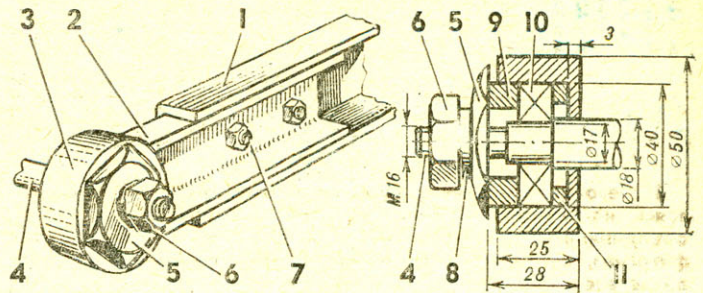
Стакан-наконечник: 1 — несущий лонжерон (швеллер 45×30), 2 — хвостовик стакана (швеллер 41×25), 3 — корпус стакана, 4 — вал звездочки, 5 — прижимная шайба (гайка М42), 6 — гайка М16×1,5, 7 — болт крепления хвостовика М8×20, 8, 9, 11 — распорные втулки, 10 — подшипник № 203.
